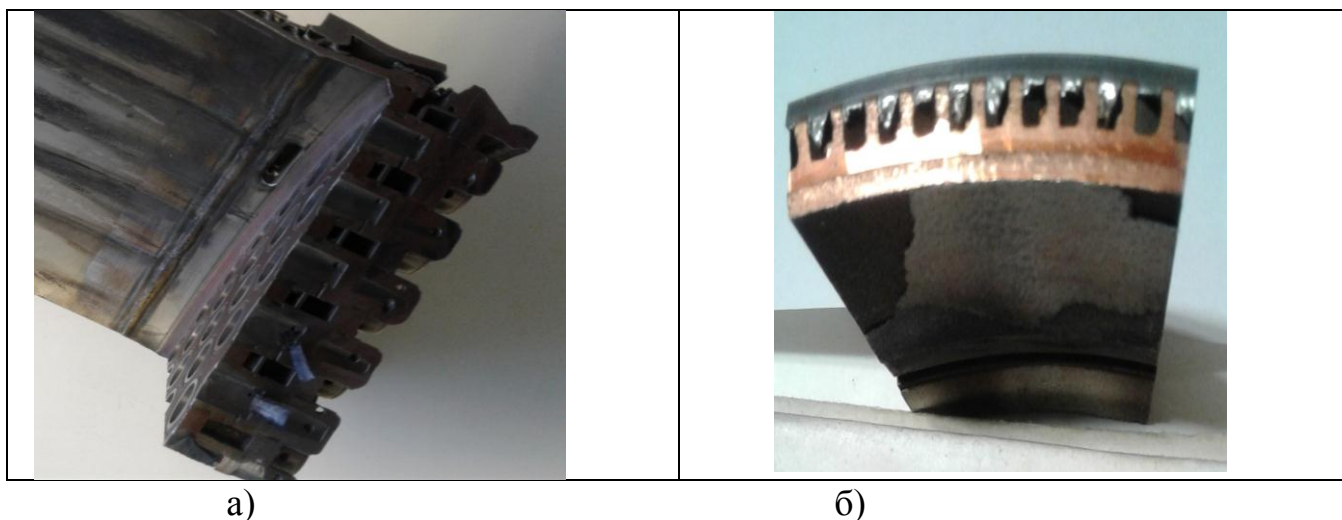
Каналы для охлаждения горячей зоны ракетного двигателя:
